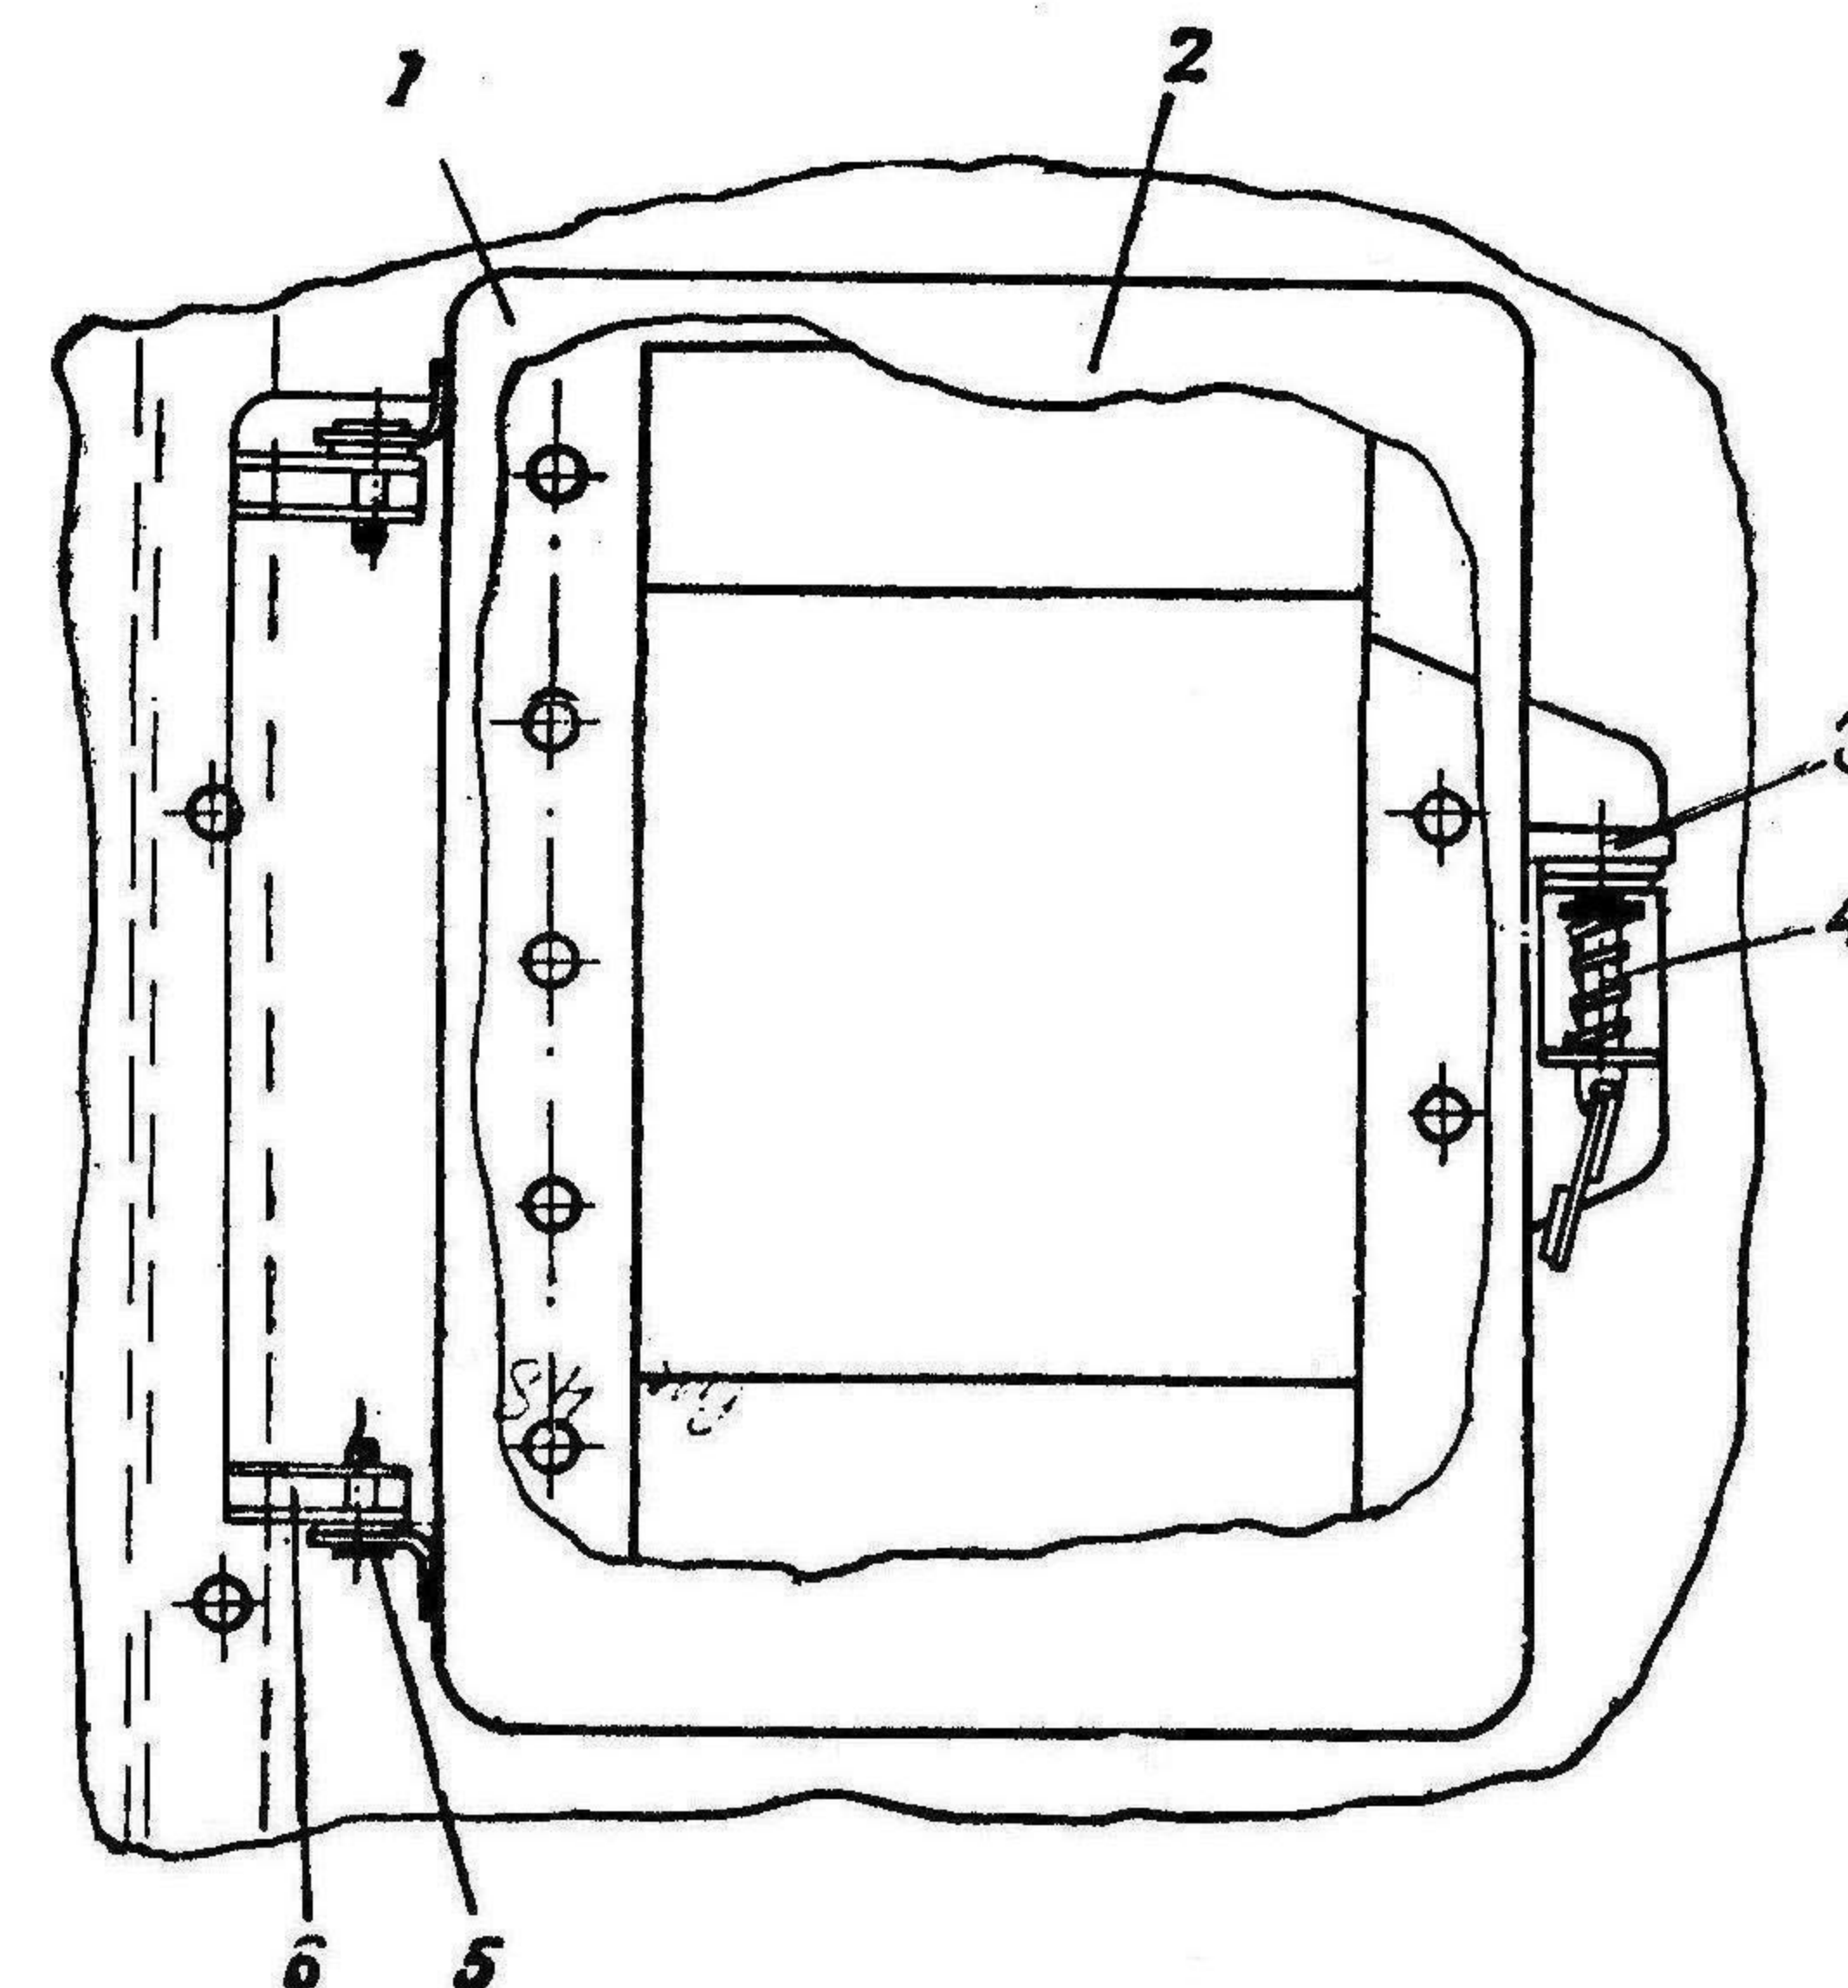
Коробка для укладки прибора ТНПО-170А:
